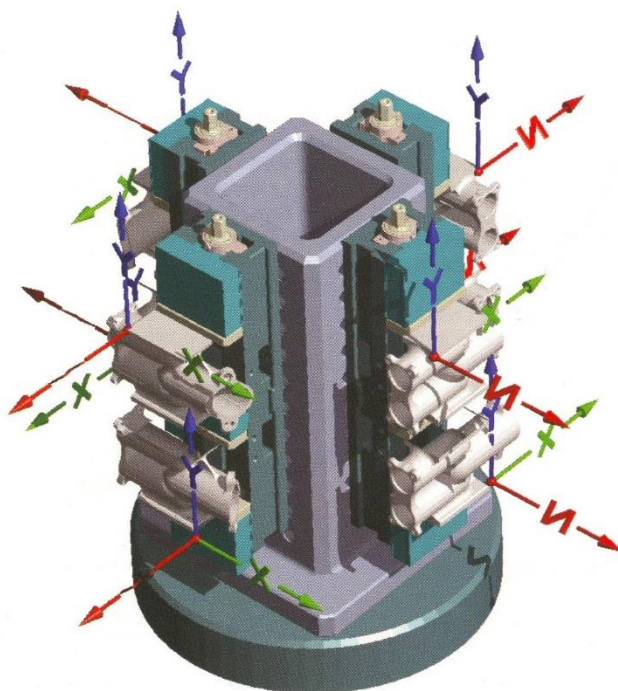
Příklad umístění nulového bodu obrobku u frézování
